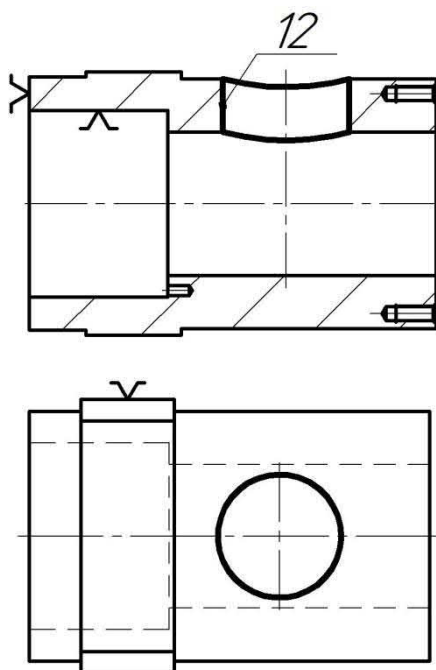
эскиз для фрезерной операции с ЧПУ 030 (установ. 3)
